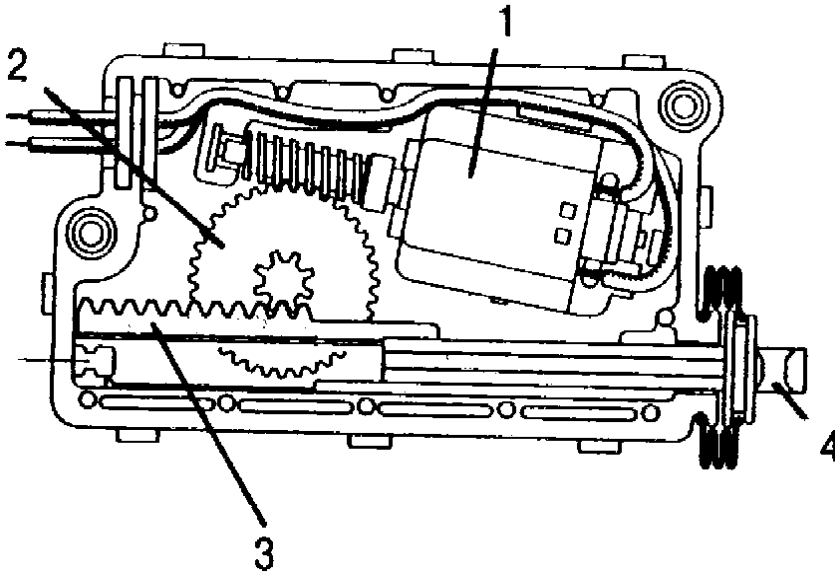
Конструкція моторредуктора блокування дверей
